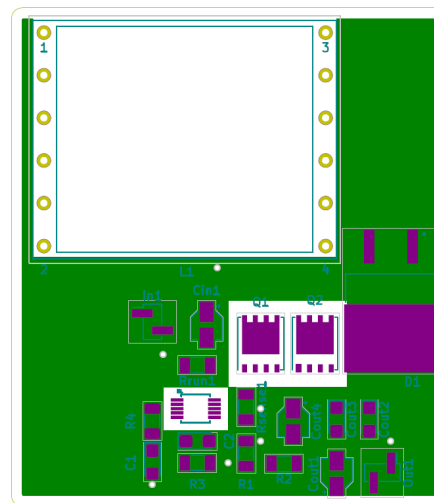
Diseño de PCB mostrando únicamente las pistas dorsales.
